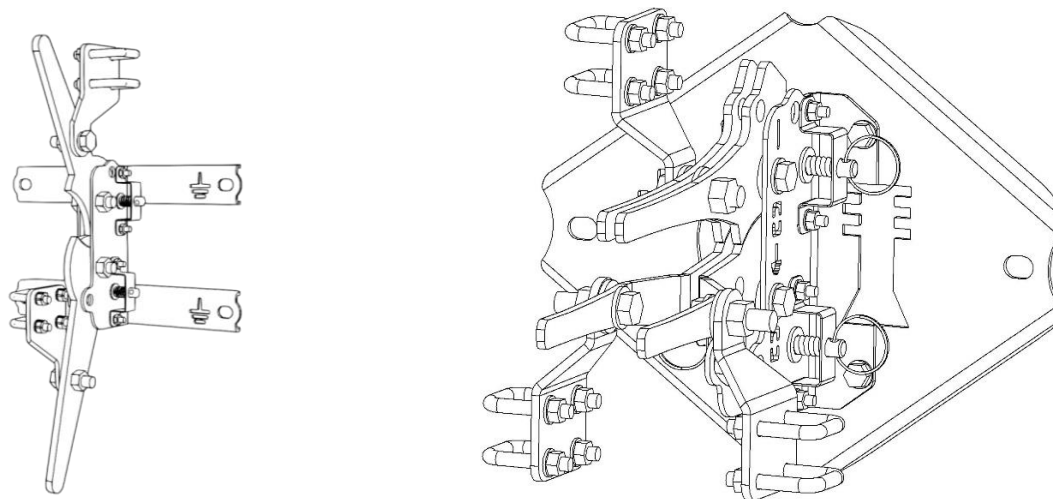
Привод для разъединителя с одним и двумя заземлителями
